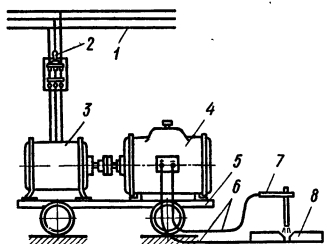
Схема электрической цепи дуговой сварки:
